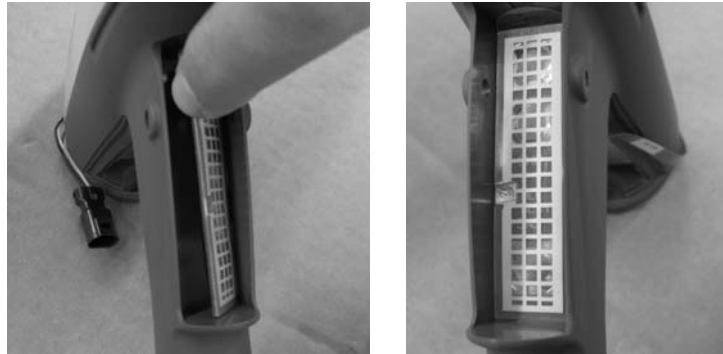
Installazione dell'interruttore del grilletto – Punto 4
